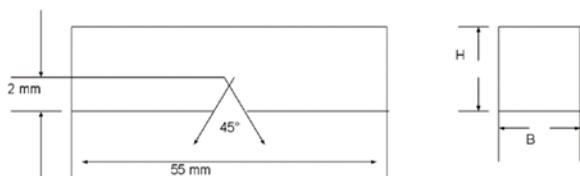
Dimensiones de la probeta Charpy en V a) SAF 2205, H = 10 mm y B = 7,5 mm [9] y b) SAF 2507, H = 10 mm y B = 5 mm [10].
